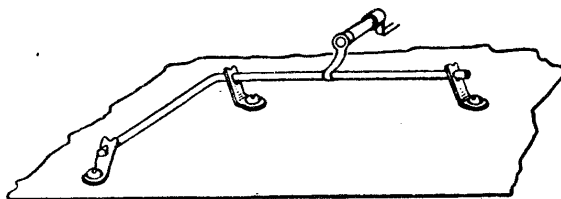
Установка и монтаж шины для заземления проводов и выводов деталей
